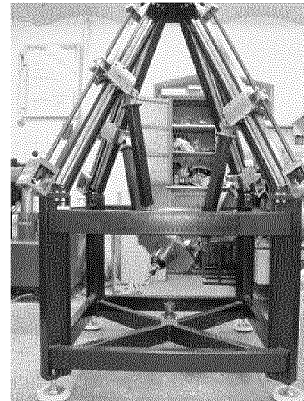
П'ятикоординатний свердильно-фрезерний верстат каркасної компоновки з МПС (КПІ)
